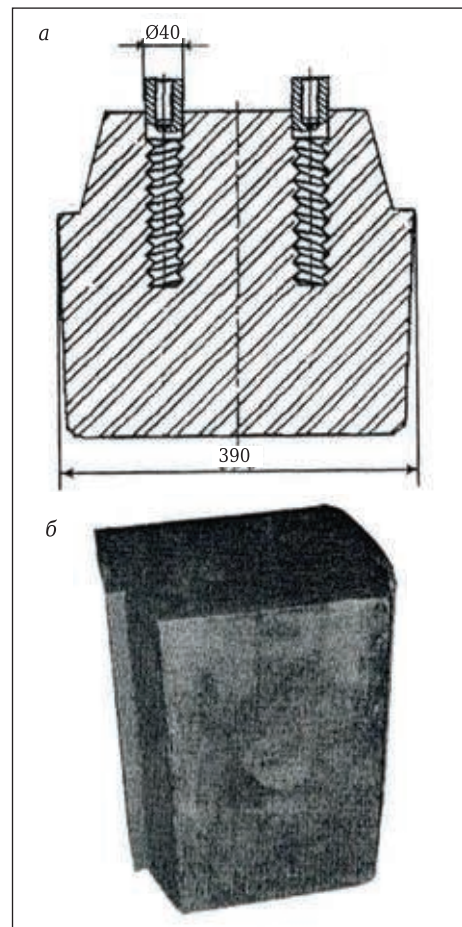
Чертеж (а) и общий вид (б) одного из типов блоков для футеровки двери коксовой печи
